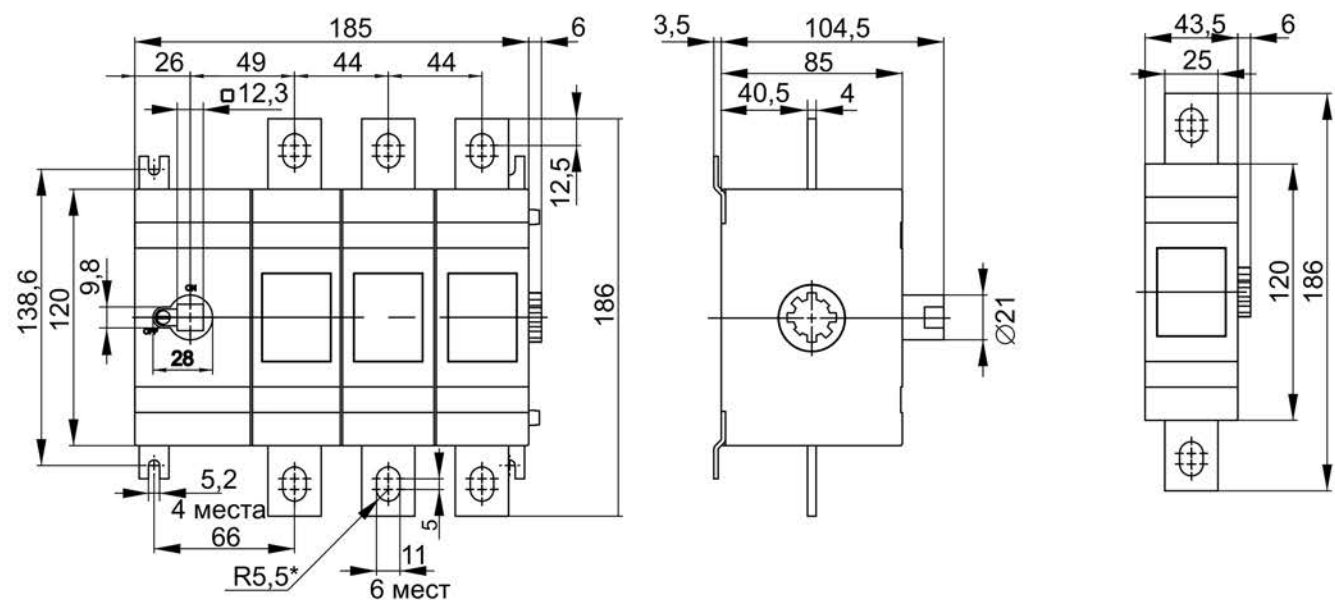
Габаритные, установочные и присоединительные размеры ВРК 315–400 А и дополнительного силового полюса 315–400 А / Figure 2 – Overall, mounting and connection dimensions of VRK 315–400 A and additional power pole 315–400 A
